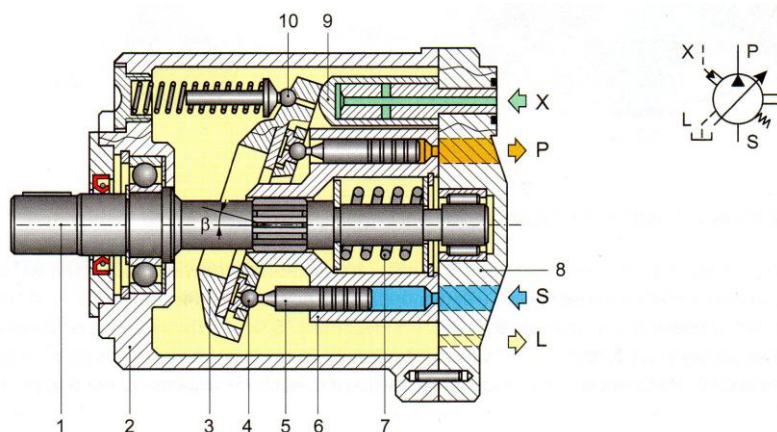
, б. Конструктивная схема аксиально-поршневого насоса с наклонным блоком: 1 – приводной вал; 2 – корпус насоса; 3 – наклонный диск; 4 – шаровой шарнир; 5 – поршень; 6 – блок цилиндров (ротор); 7 – пружина; 8 – крышка; 9 – управляющий поршень; 10 – подпружиненная опора; S, P – каналы всасывания и нагнетания; β – угол наклона диска к оси вращения приводного вала.
